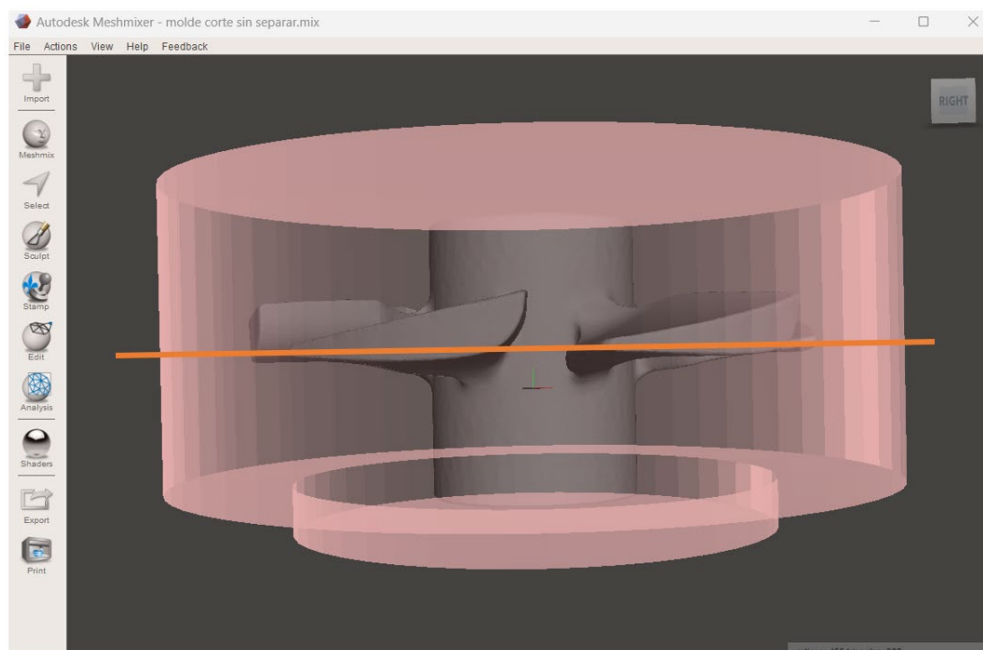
Plano de corte para la apertura del molde indicado mediante la línea naranja.
